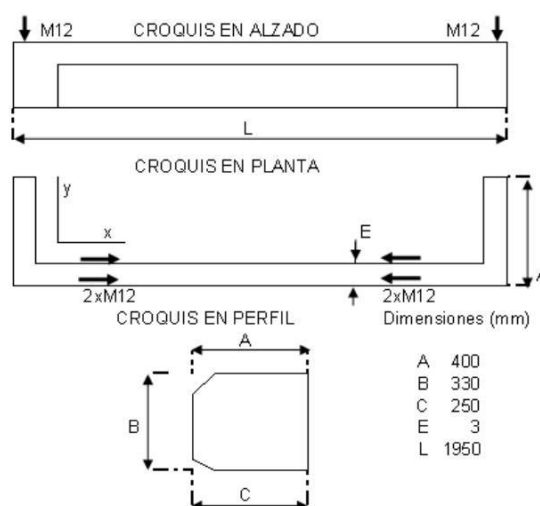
Alçat, planta i perfil del para-xocs davanter original
